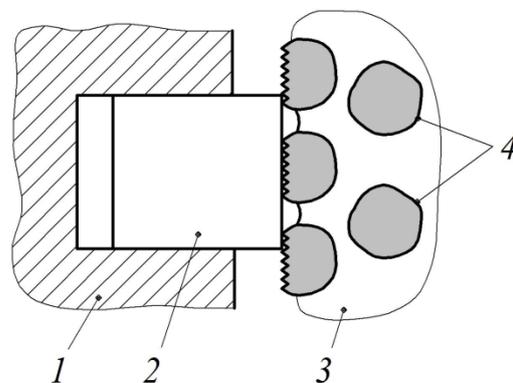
Схема взаимодействия поршневого кольца с рабочей поверхностью цилиндра: 1 – поршень; 2 – поршневое кольцо; 3 – цилиндр блока из алюминиевого сплава; 4 – кристаллы кремния
